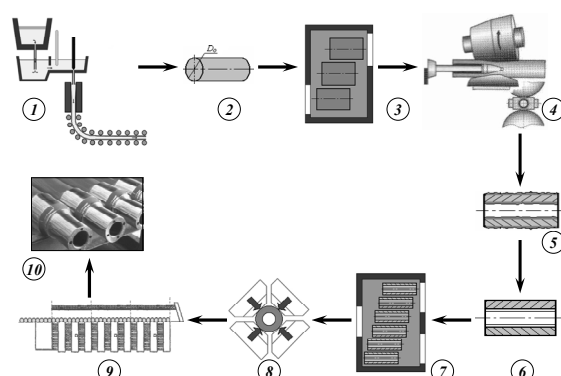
Вариант технологии изготовления полрой оси из сплошной непрерывнолитой заготовки круглого сечения (прошивка - ковка)
